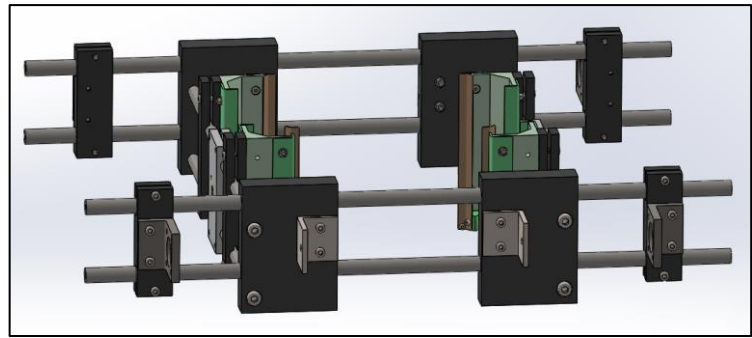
Montaje grupo de piezas de apoyo (SE)
